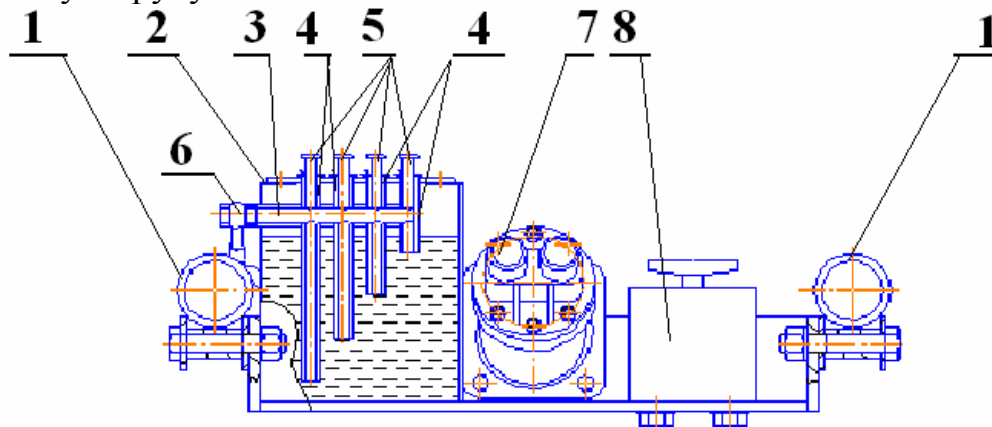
Схема гидробака с приспособлением для исключения вылива масла при обрыве рукава высокого давления: 1 – рама самоходного шасси, 2 – гидравлический бак, 3 – горизонтальная труба, 4 – вертикальные патрубки, 5 – заглушки, 6 - трубопровод к насосу всасывающий, 7 – насос 210.20, 8 – предохранительный клапан КПЕ – 20
